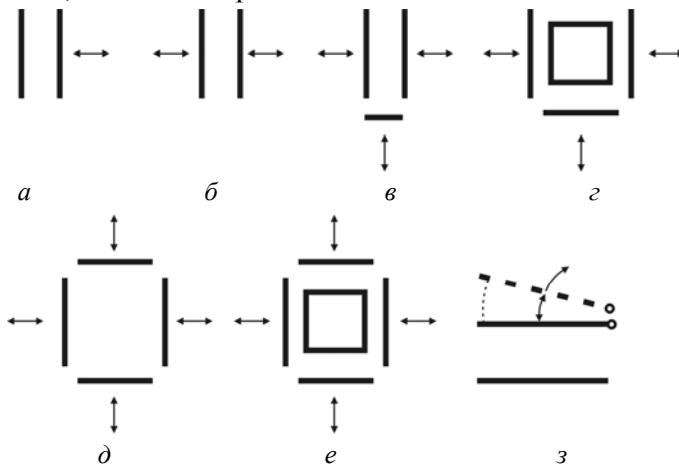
Схеми розташування плит на машинах для лиття в металеві форми різної конструкції:
